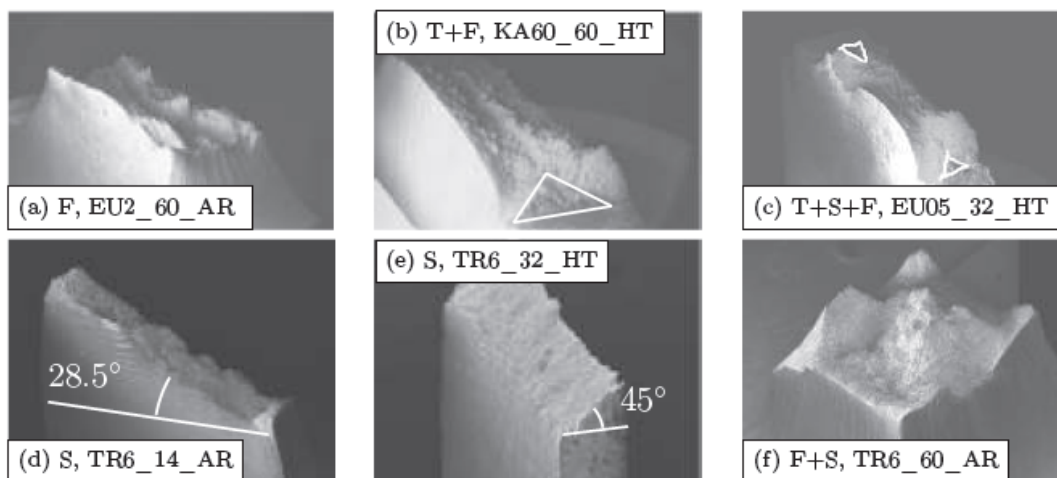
Surface de rupture macroscopique, (a) éprouvette faiblement entaillée en U, (b) éprouvette Kahn, (c) éprouvette EU05L\_32, (d), (e), (f) éprouvette TR6 [66]
